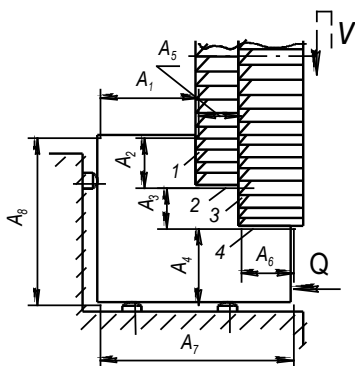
Схема обробки поверхнь заготовки (до задачі 4).
